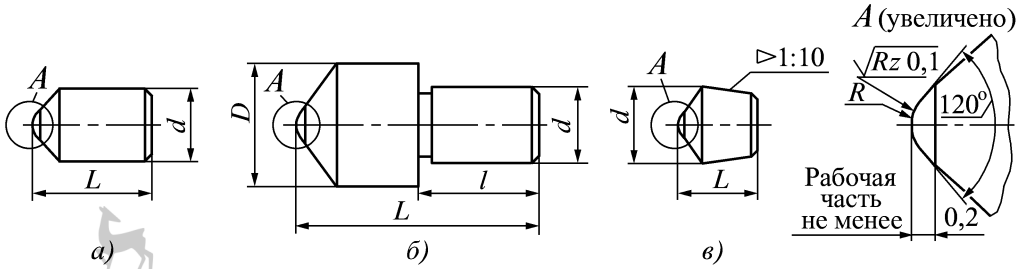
Формы рабочей части алмазов выглаживающего инструмента
